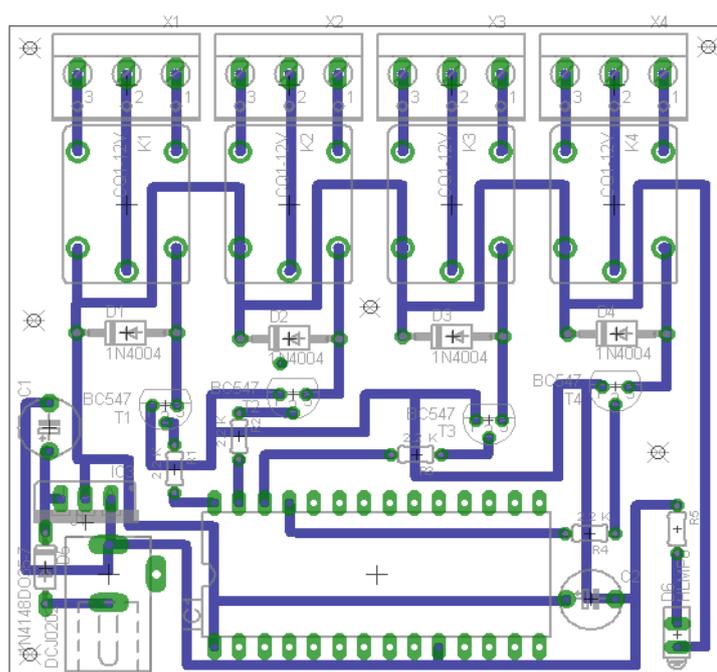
Layout* da placa de quatro relés pronta para ser fresada.
